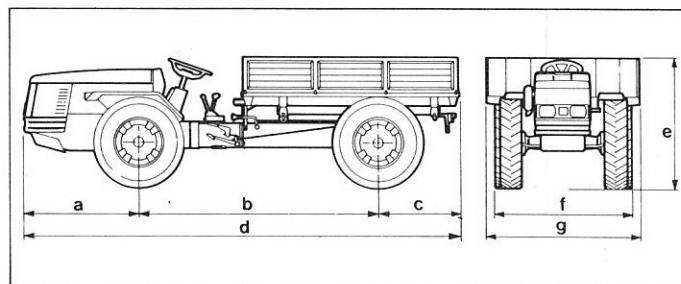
Dimensions hors tout du Unicar - Unitrans - Tigrecar.
